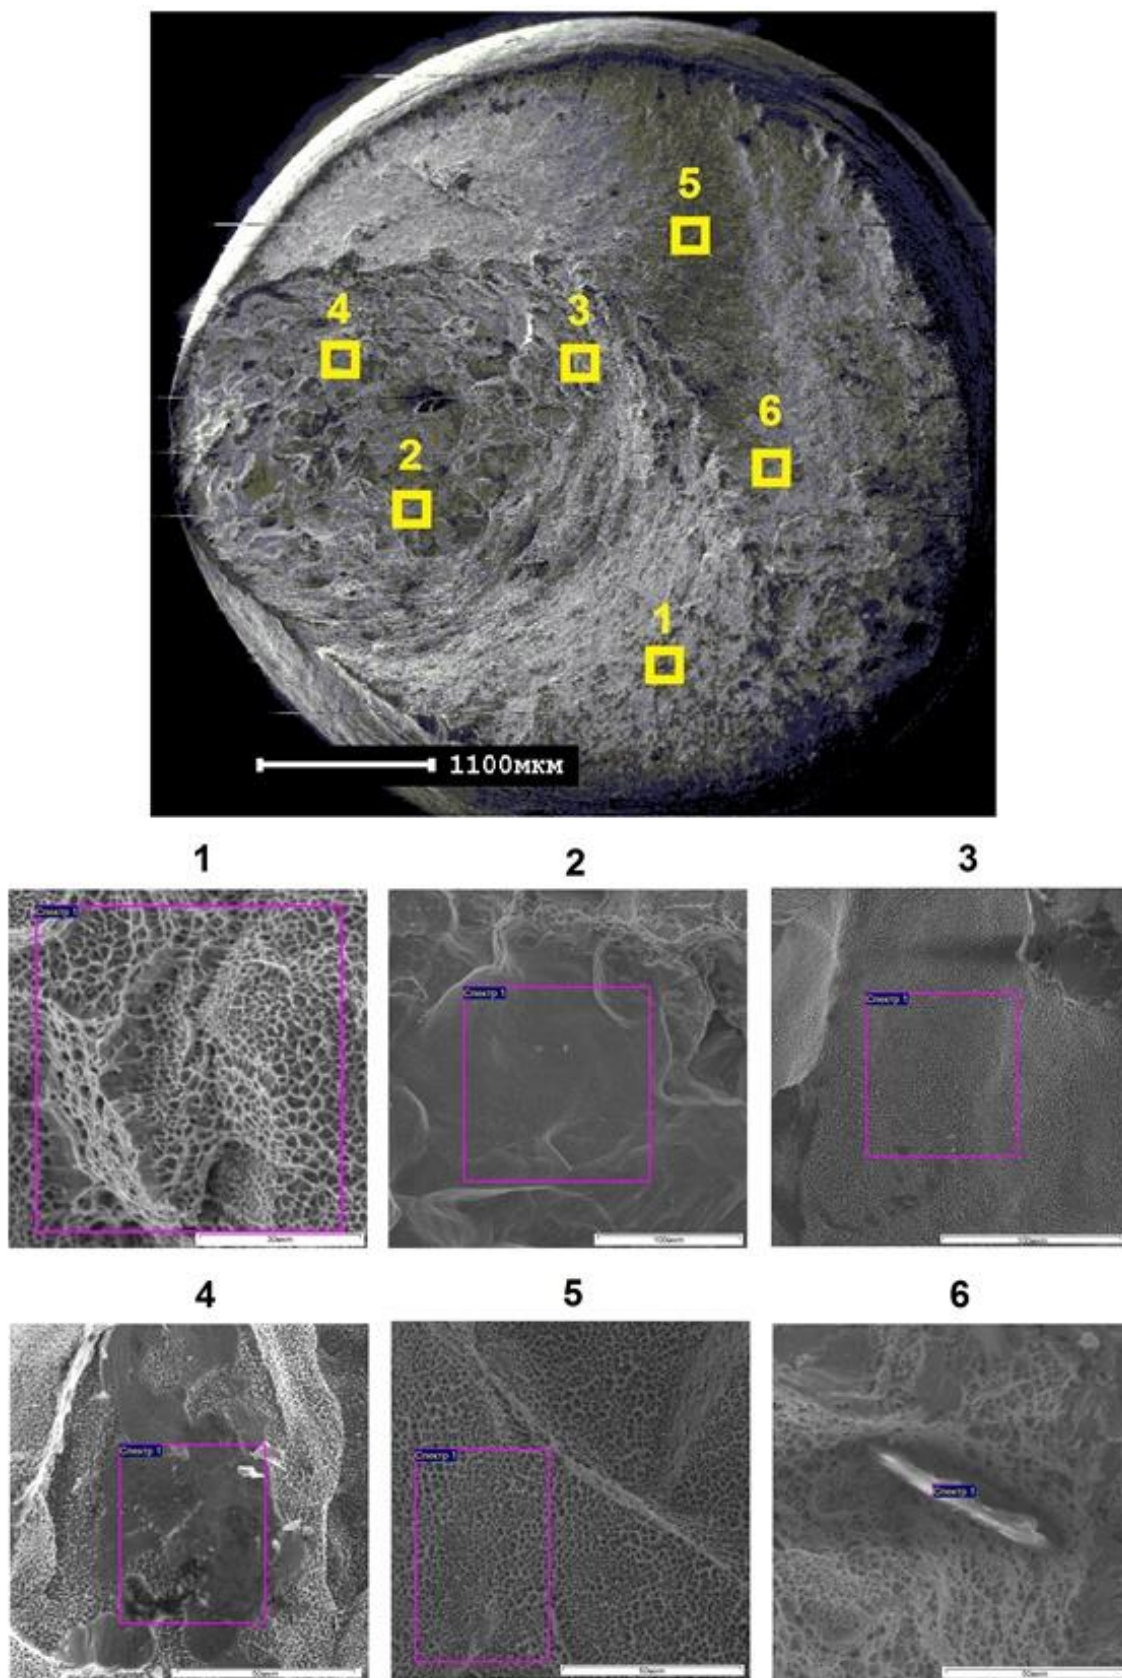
Фрактограмма поверхности излома образца на растяжение металла шва, выполненного сварочной проволокой марки Св-15ХЗГМФТА в сочетании с флюсом 48АФ-71
